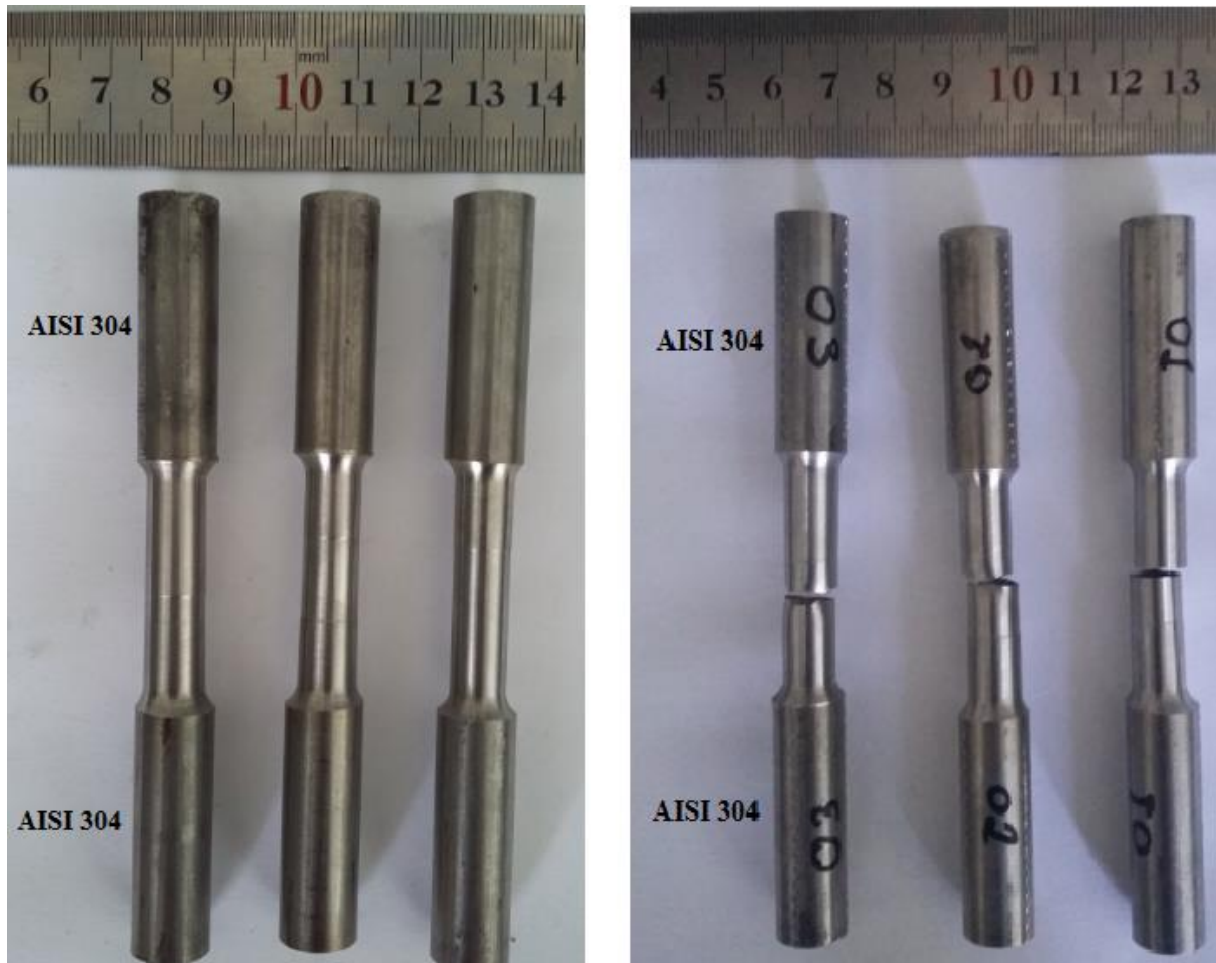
Corpo de prova 18; 2-3-3. Soldagem similar do aço AISI 304 e ensaio de tração
